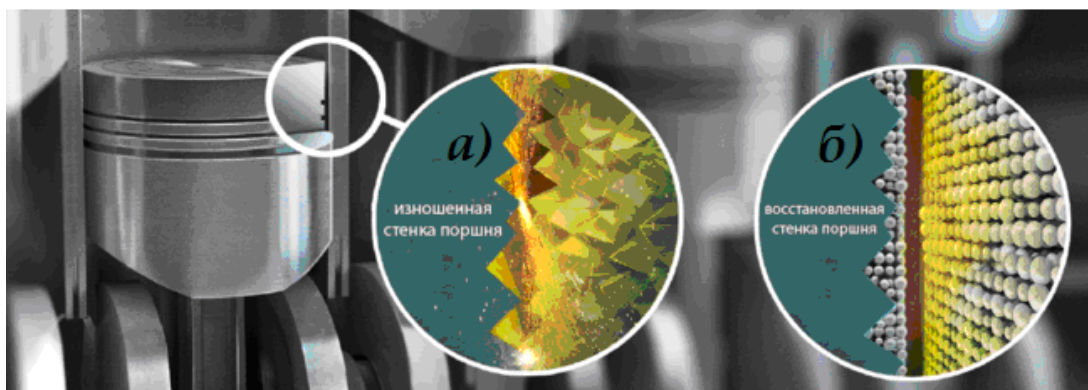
Особливості поверхні деталі: а) без присадки; б) з хімічно активною присадкою
